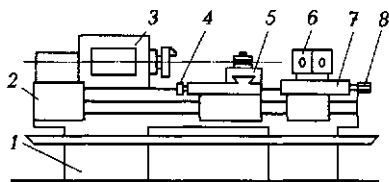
Патронный токарно-револьверный полуавтомат:
